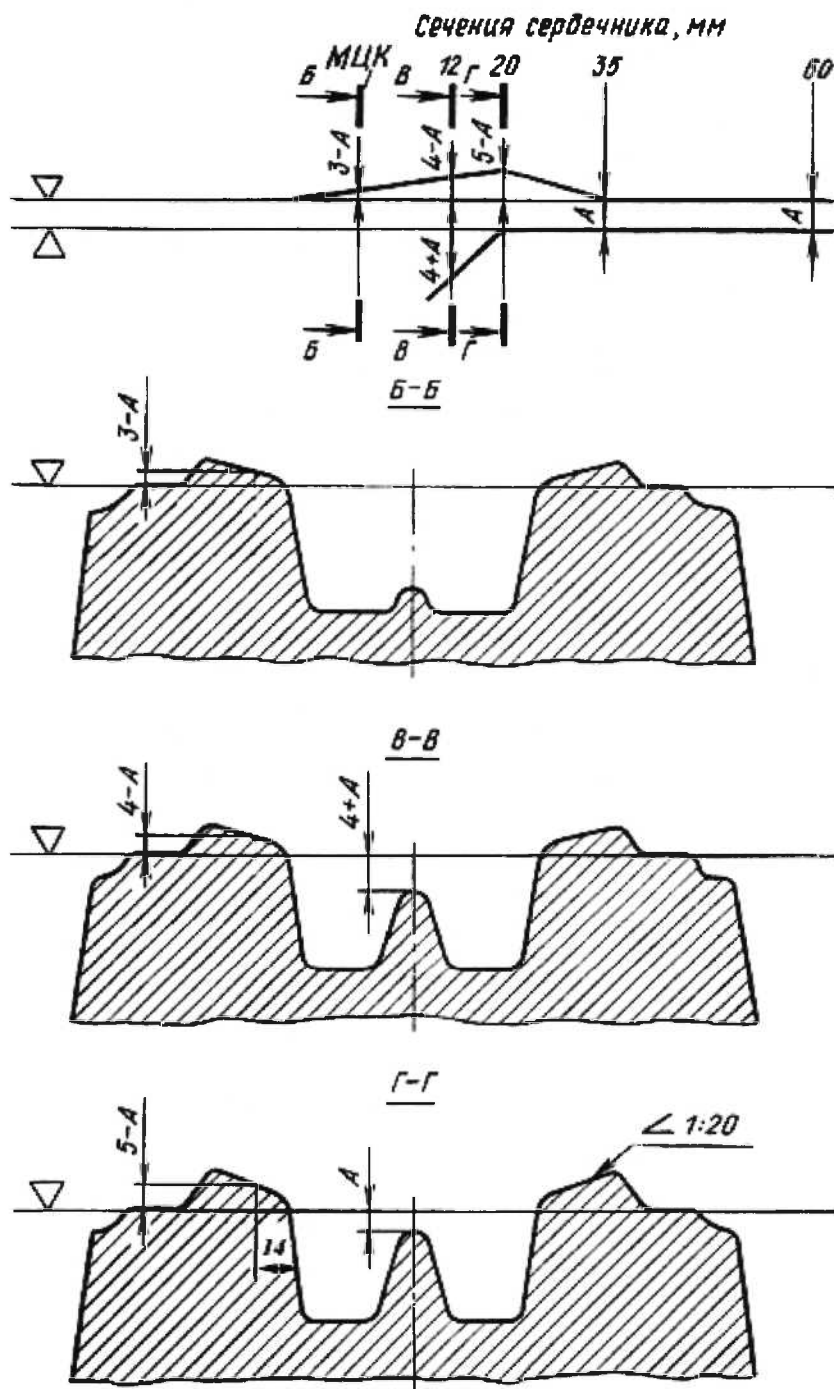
Продольный и поперечный профили наплавленных цельнолитых крестовин типа Р65 марок 1/11 и 1/18 после обработки:
